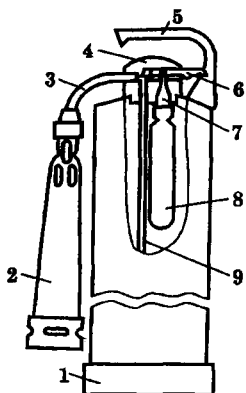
Огнетушитель воздушно-пенный ОВП-10: 1 — корпус; 2 — пенный насадок; 3 — трубка; 4 — крышка; 5 — рукоятка; 6 — пусковой рычаг; 7 — шток; 8 — баллончик со сжатым воздухом; 9 — сифонная трубка
